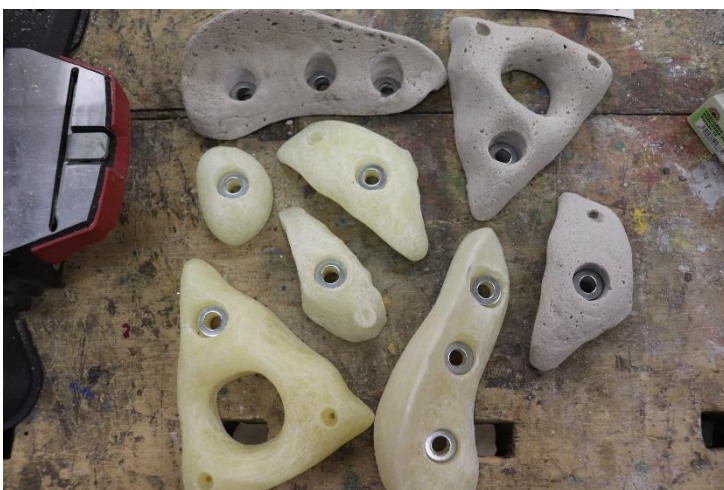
Obrušování detail 2 (vlastní zdroj)
